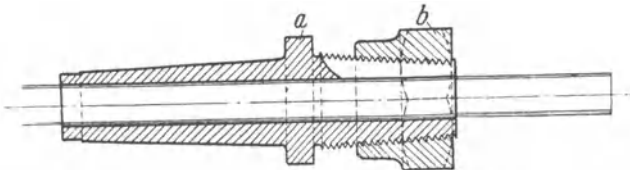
Klemmfutter mit konischem Gewindeanzug.
